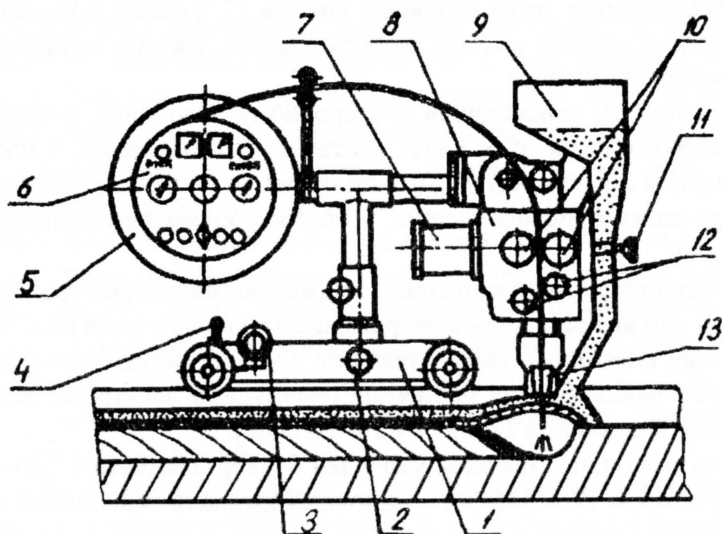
Устройство сварочного трактора-автомата АДС-1000:
